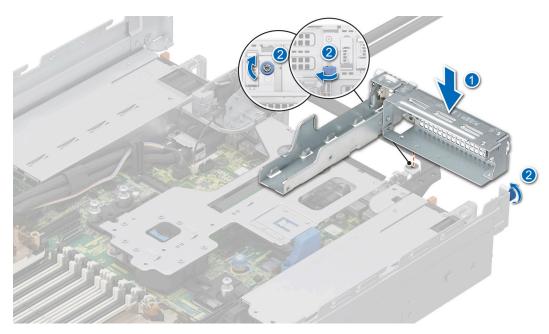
Einsetzen des Platzhalters für Riser 1
